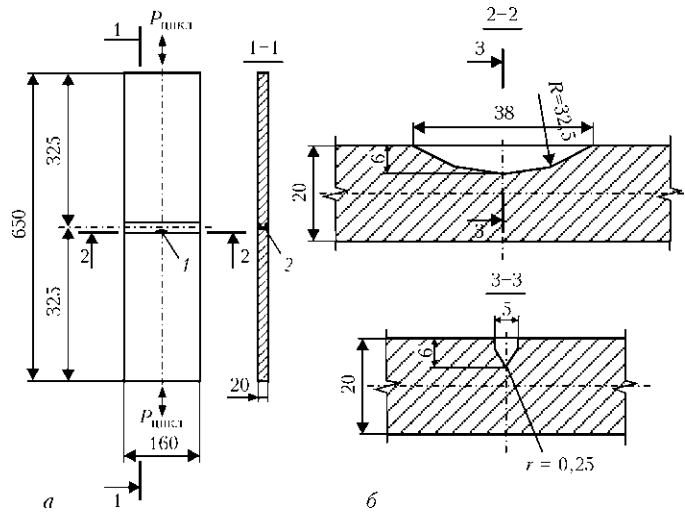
Схема (а) и размеры (б) образцов сварных соединений стали 06ГБ для испытания на циклическую трещиностойкость: 1 — надрез по линии сплавления в ЗТВ; 2 — усиление шва снято с двух сторон
